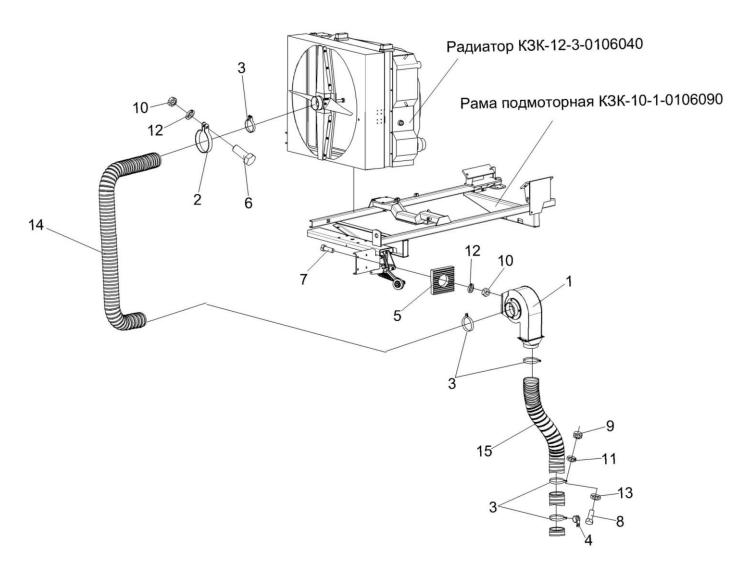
Установка вентилятора КЗК-12-3-0112240
